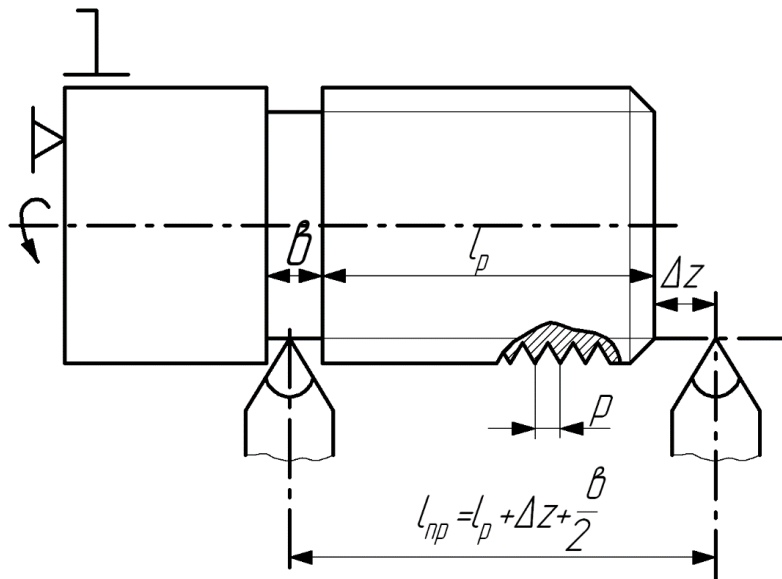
Схема для визначення шляху робочого ходу різьбового різця
